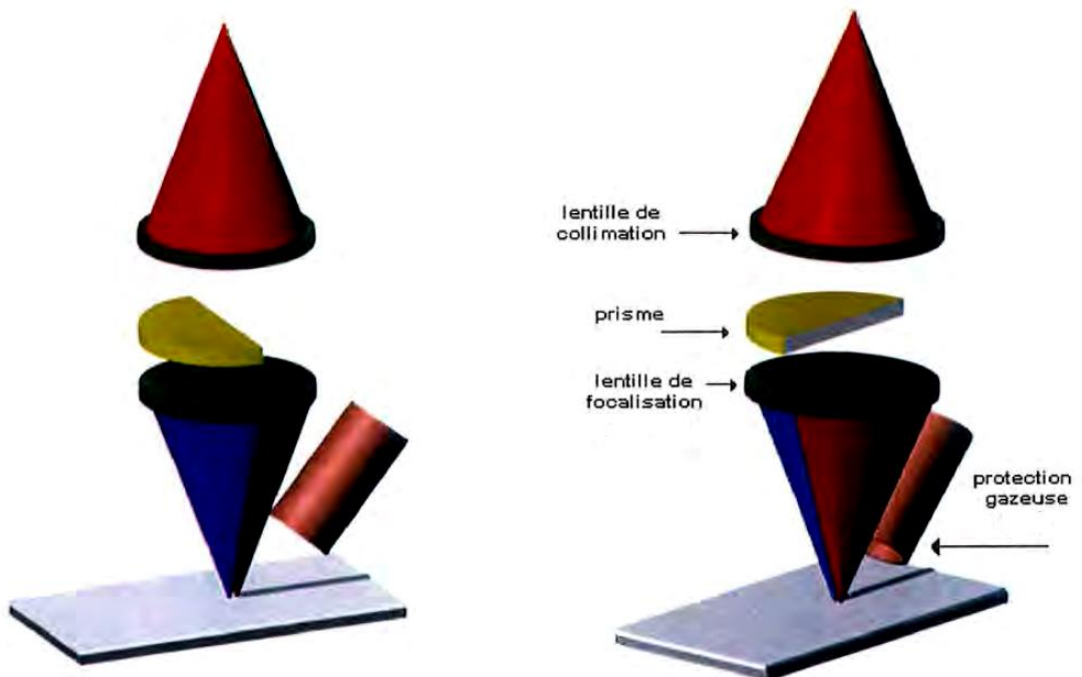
Schéma de principe de soudage laser en configuration bispot
